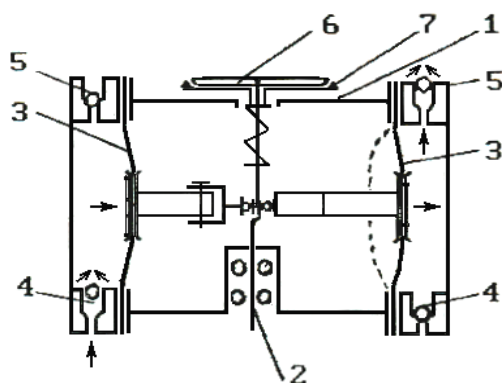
Схема роботи насоса-дозатора робочої рідини:
